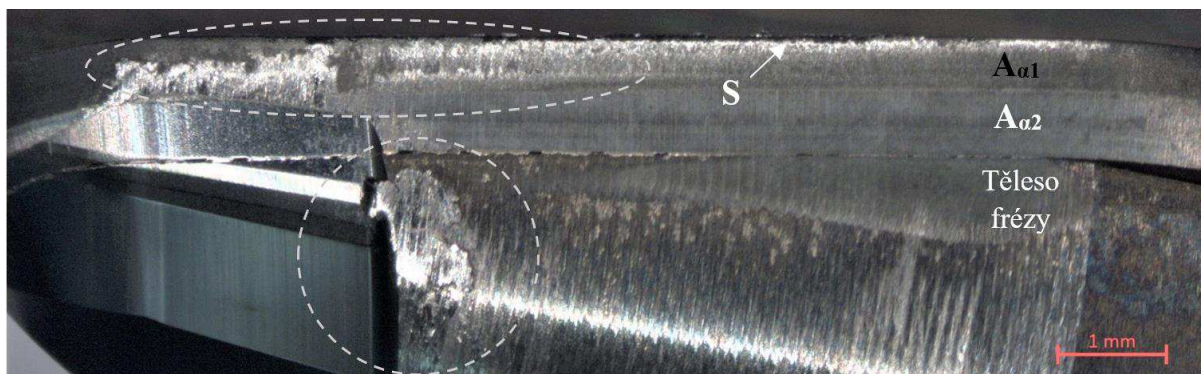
Opakované odbroušení SK tělesa DP frézy, které třelo o obrobený povrch.
